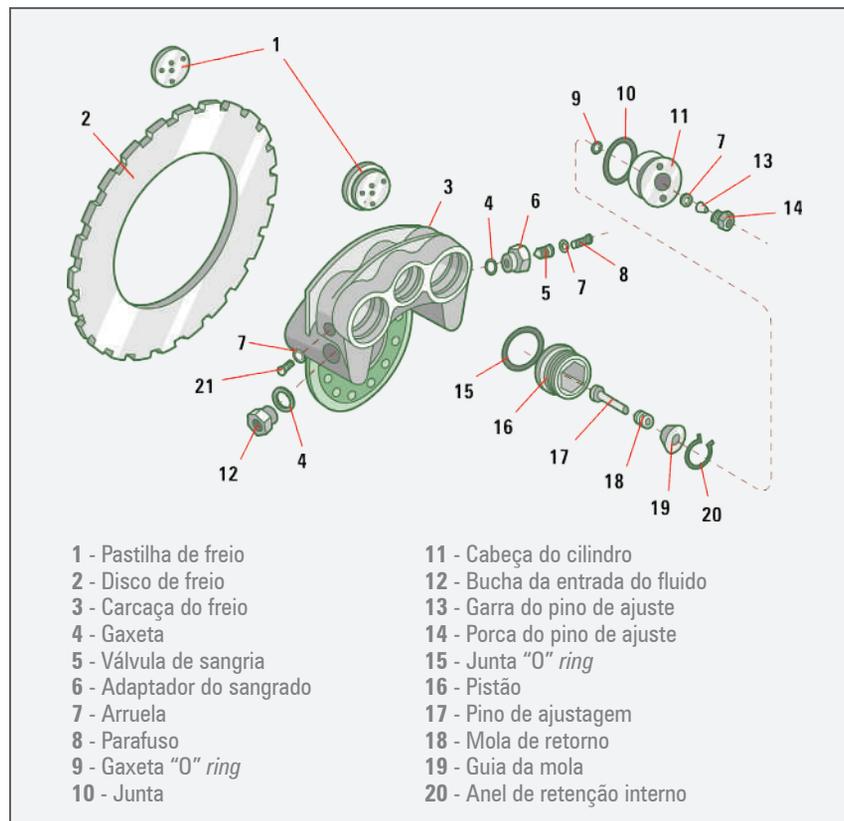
Vista explodida de um conjunto de freio de disco simples (monodisco)
